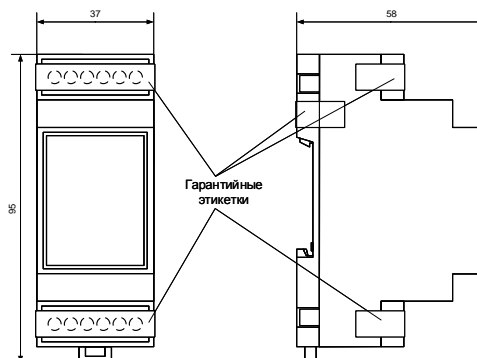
Внешний вид, габаритные и установочные размеры счетчика СИПУ xxx.2x.D,
